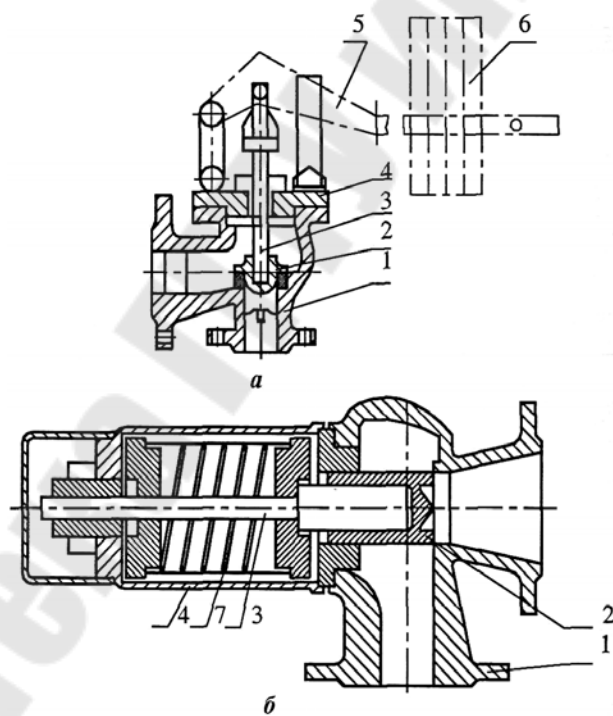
Предохранительные малоподъемные клапаны: а - однорычажный фланцевый, тип 17чЗбр; б - пружинный фланцевый, тип 17с11нж; 1 - корпус, 2 - затвор, 3 - шпindelь, 4 - крышка, 5 - рычаг, 6 - груз, 7 - пружина
